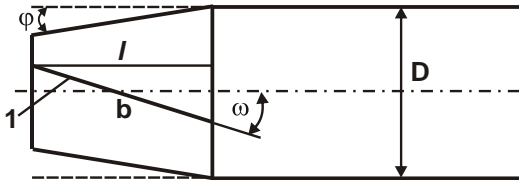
Розрахункова схема геометричних параметрів забірної частини розвертки: 1 – зуб розвертки
